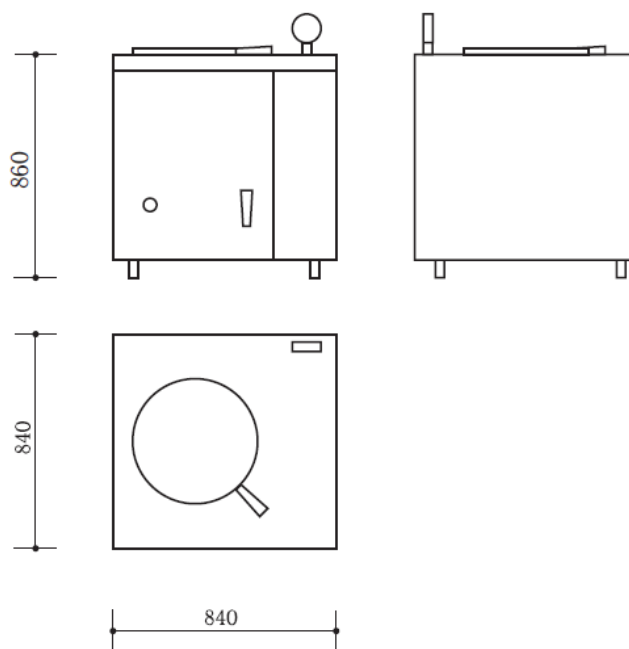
Габаритные размеры котла пищеварочного КПЭМ-100
